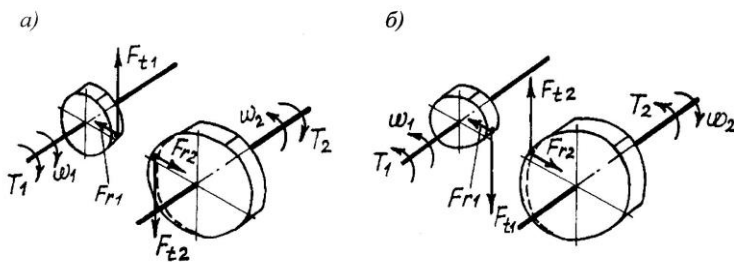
Схема сил в зацеплении прямозубой цилиндрической передачи
